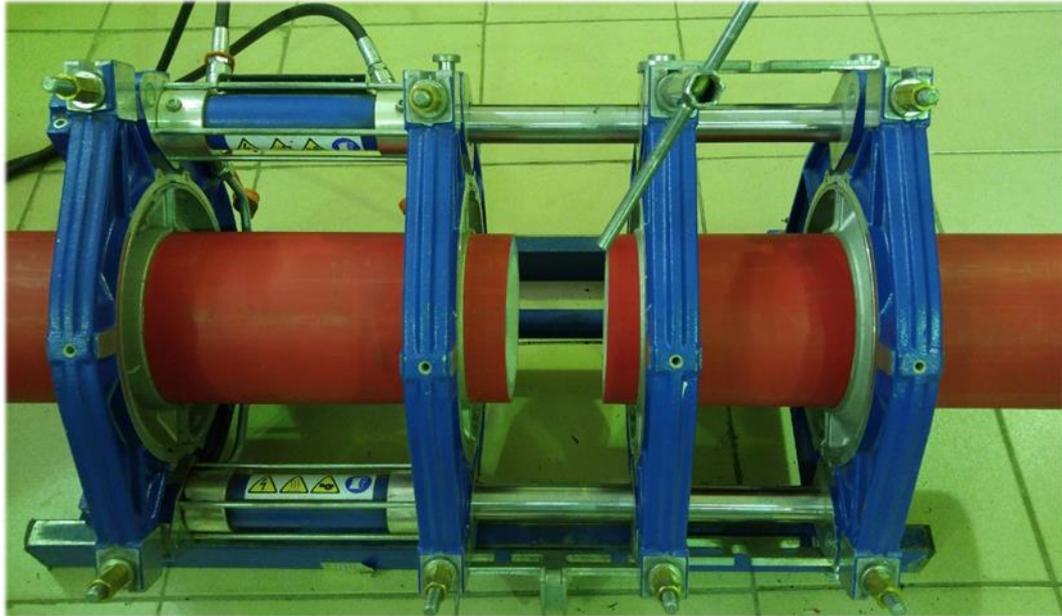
Фиксация труб в центраторе сварочного аппарата
